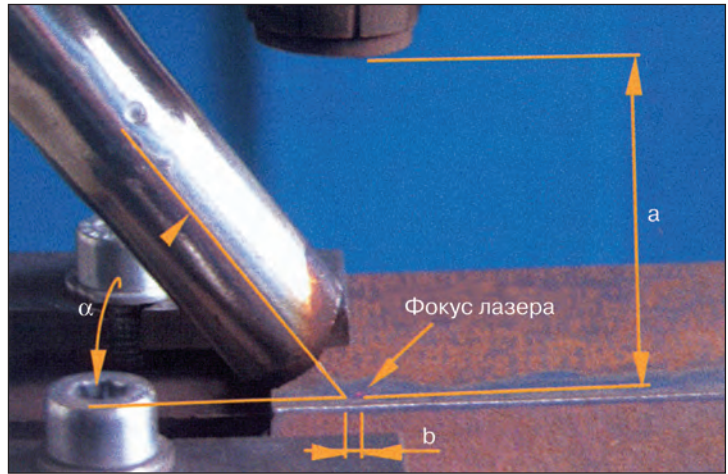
Взаимное расположение лазерной головки и сварочной дуги при гибридной сварке: a — рабочее расстояние лазерной головки (50 мм); b — смещение лазерного луча (2 мм); α — угол наклона MAG сопла ($\alpha=55^\circ$)
